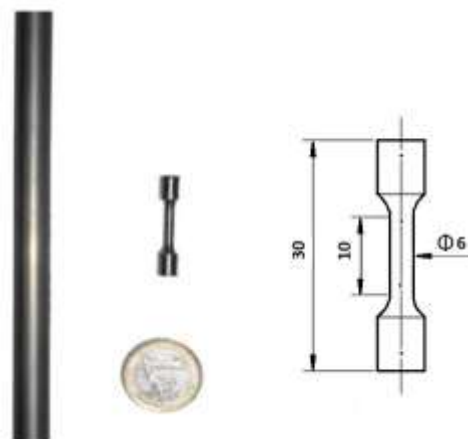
De izquierda a derecha: barra extruida, muestras cilíndricas de tracción mecanizadas y dimensiones de las mismas.
